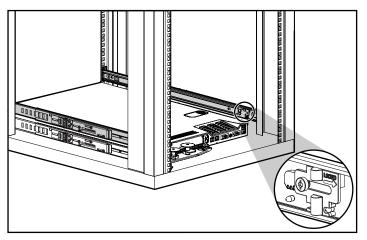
Rails universels installés dans le rack, prêts pour l'installation du serveur (vue arrière) et dispositif de blocage des rails en position verrouillée.
